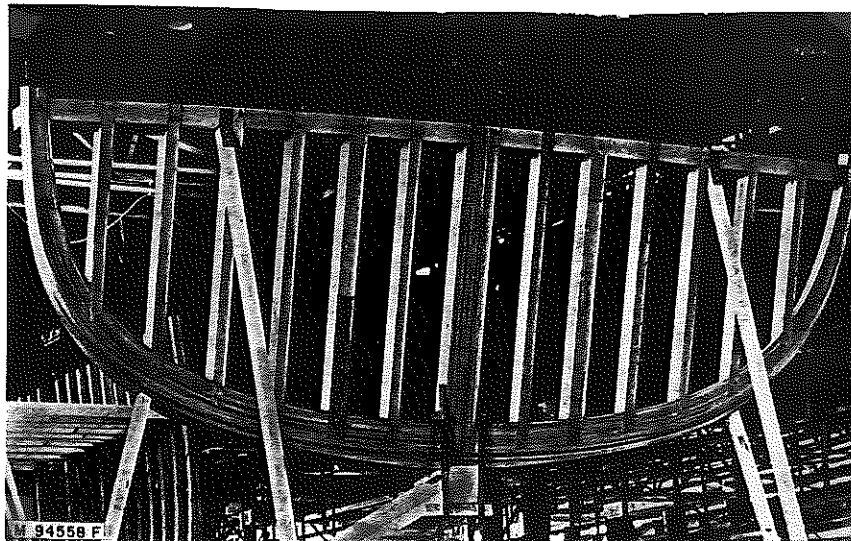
Estrutura da seção principal de um "caça-minas" - madeira laminada (14).
